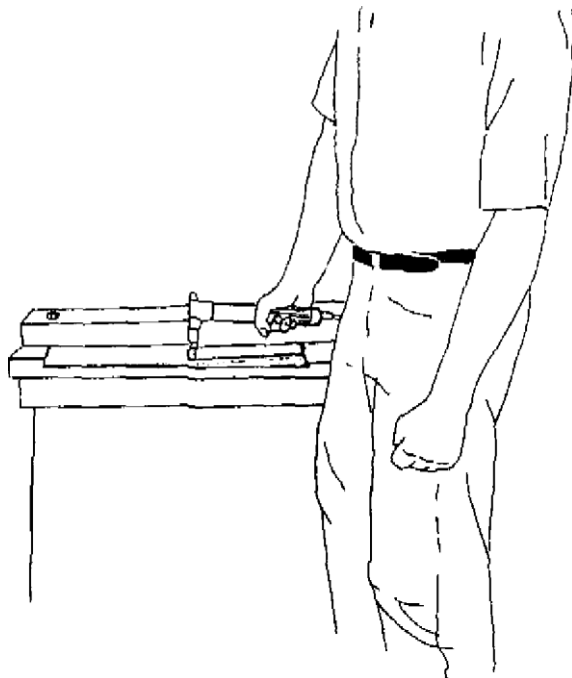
Вирубні ножиці та ножиці. Робоче положення оператора
